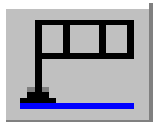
Позначення бази і допуску розташування поверхні
